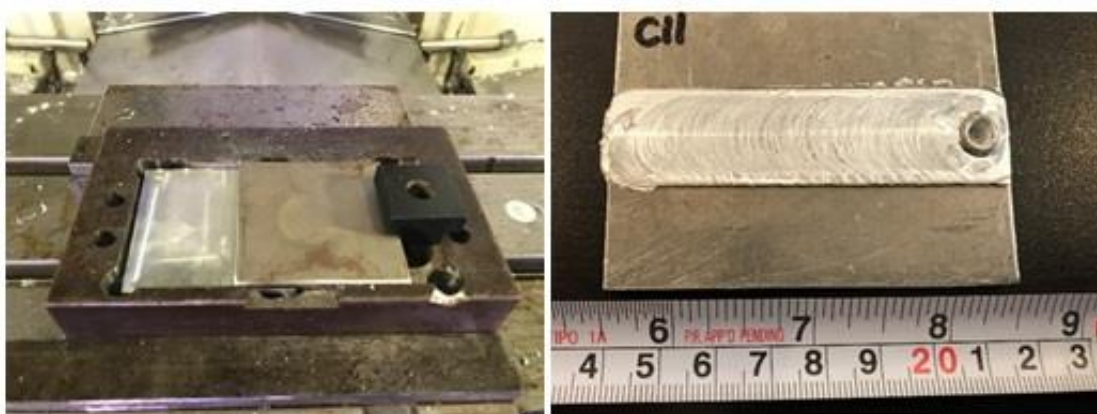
Prueba realizada por el proceso de soldadura FSW
